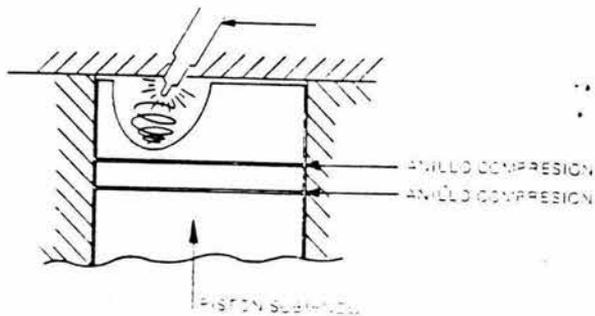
Inyección Indirecta. La Inyección se hace sobre la Cámara de Combustión Maquinada en el Pistón.
